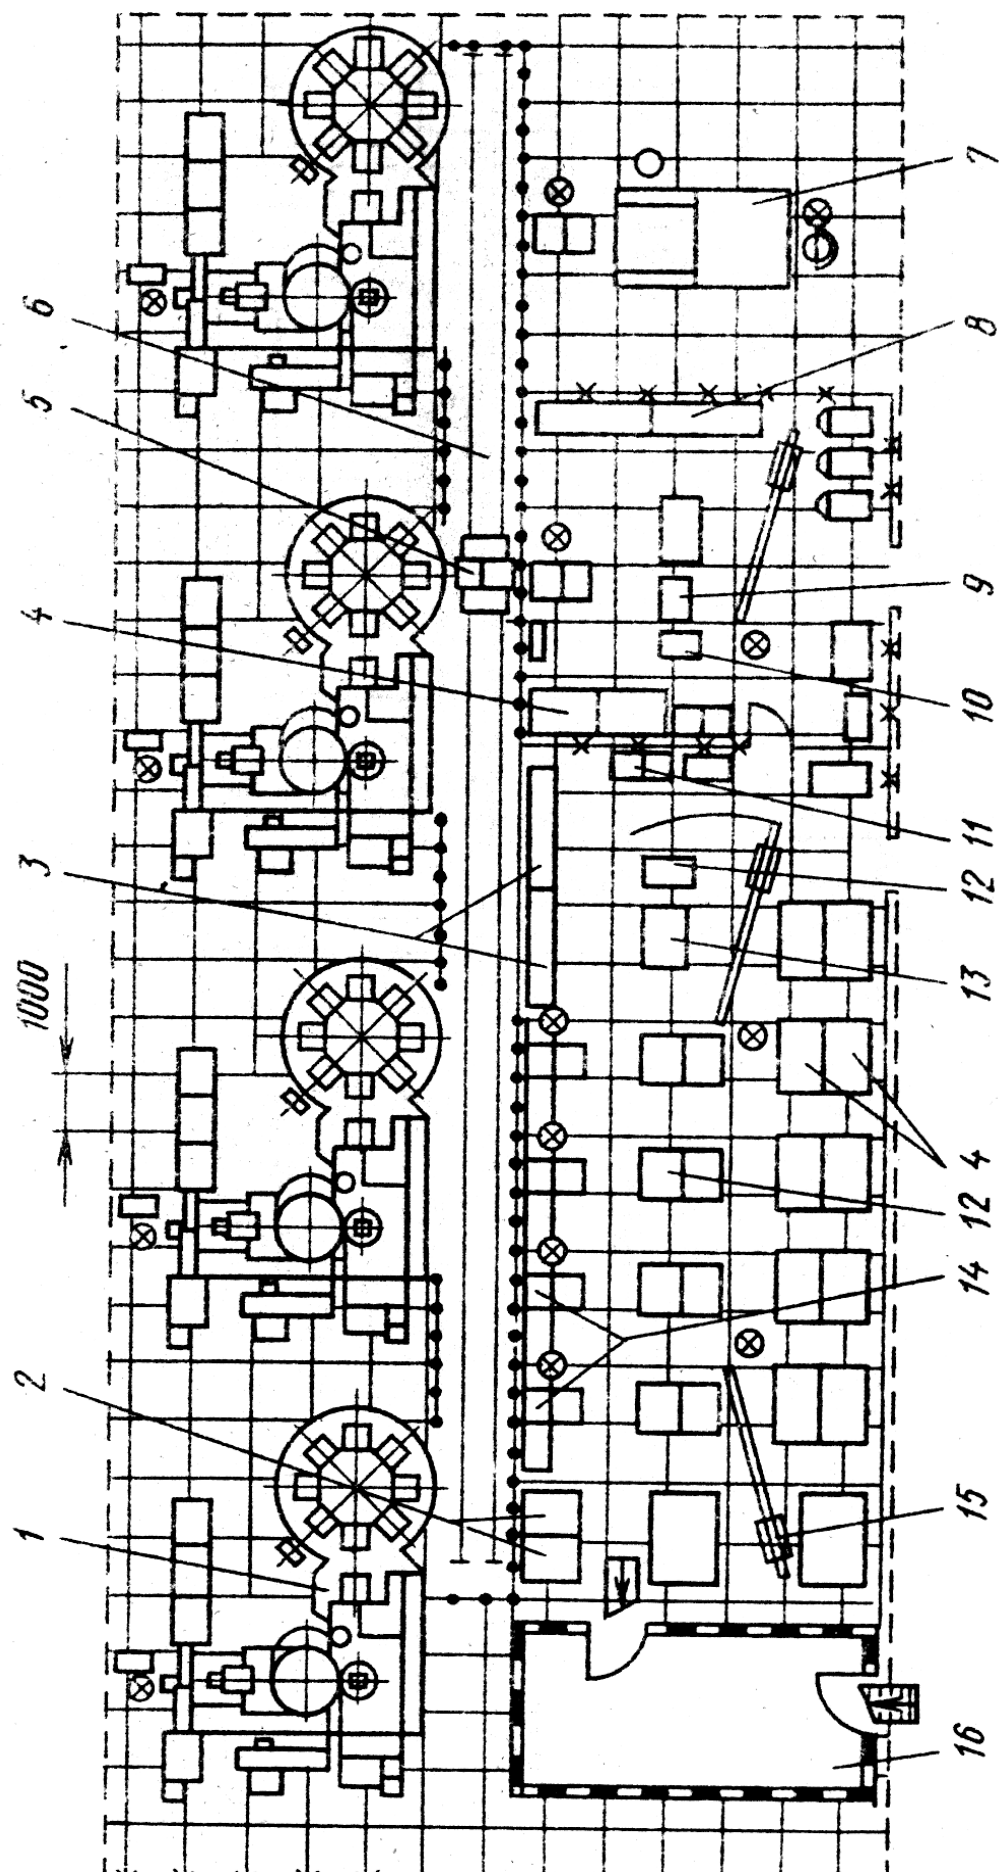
Планировка ГПС для изготовления корпусных деталей
